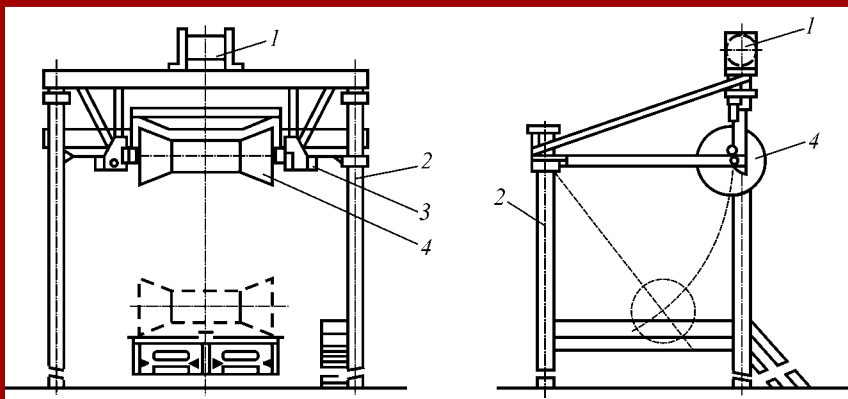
Установка статического действия для разравнивания и уплотнения угля в полувагонах: 1 — подъемный механизм; 2 — рама; 3 — стопорное устройство; 4 — каток-уплотнитель
